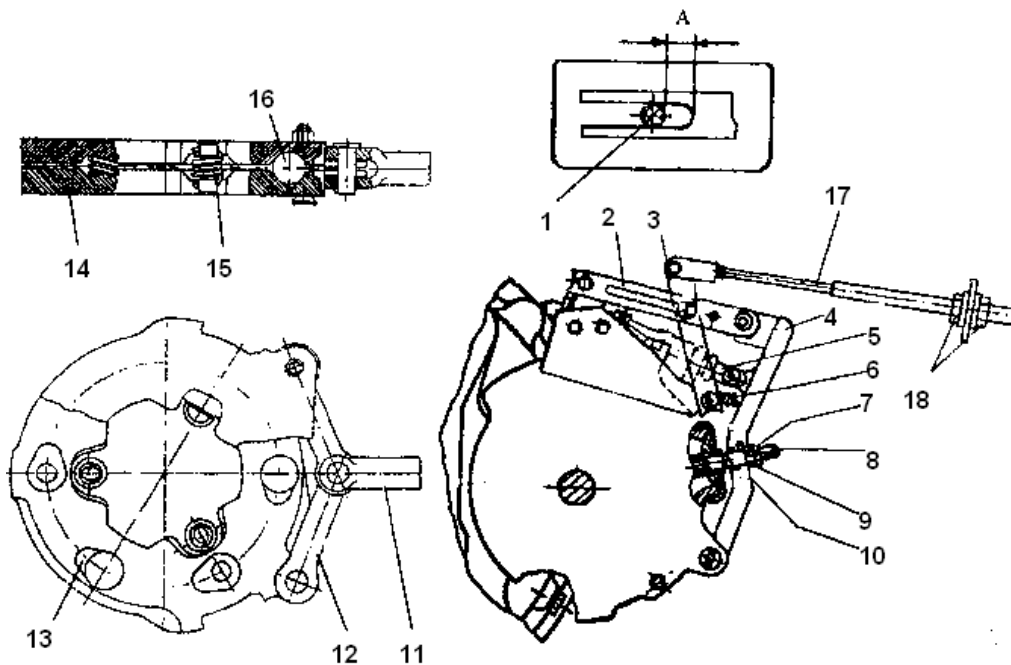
Дисковый тормоз: 1 – ось; 2 – рычаг; 3 – рычаг привода стояночного тормоза; 4 – рычаг тормоза; 5 – толкатель; 6, 15 – пружина; 7 – контргайка; 8 – шпилька; 9 – гайка; 10 – сферическая шайба; 11 – вилка; 12 – тяга дисков; 13 – лунка; 14 – диск нажимной; 15 – пружина; 16 – шарик; А – регулируемый зазор (3...5 мм); 17 – трос
